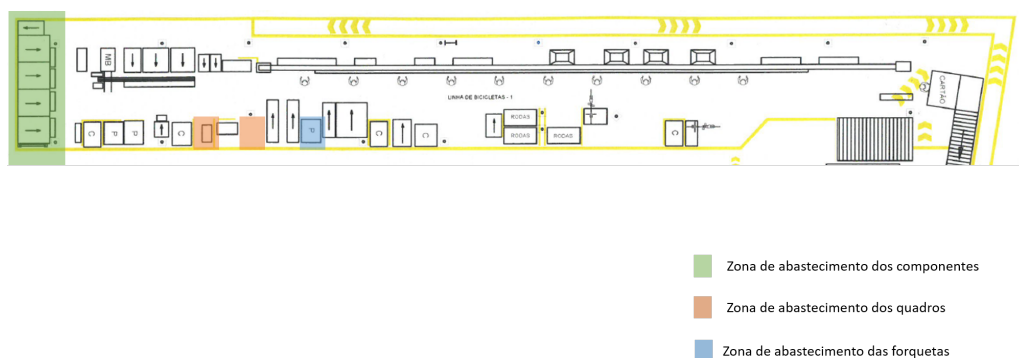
Planta da linha 1 com zona de abastecimento assinalada
